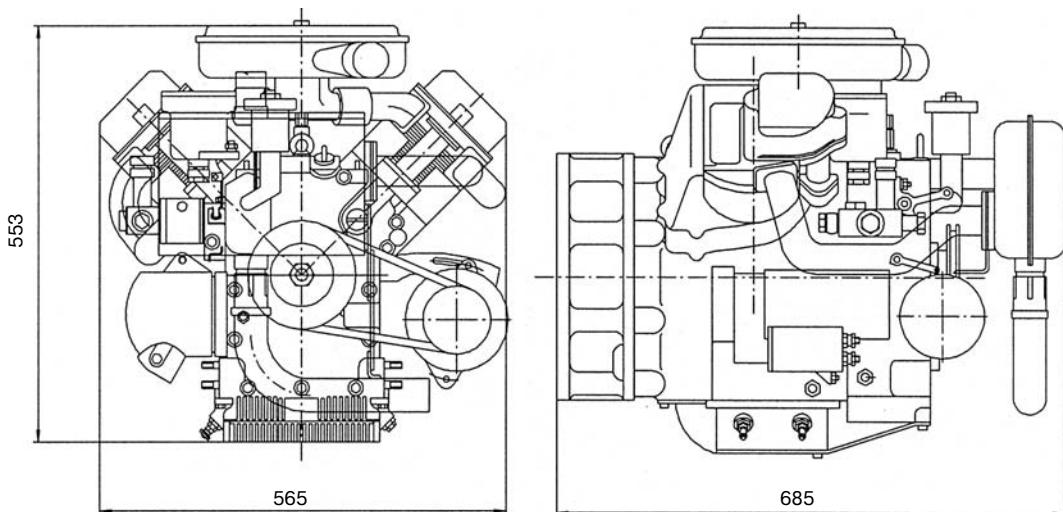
Габаритные размеры двигателя В2Ч8,2/7,8
